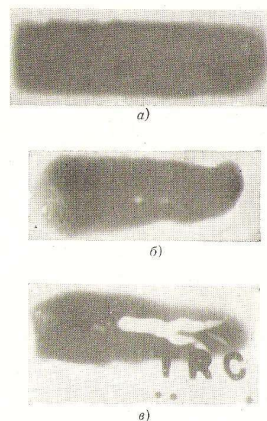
Изломы металла отливок, отлитых из перегретого сплава.
